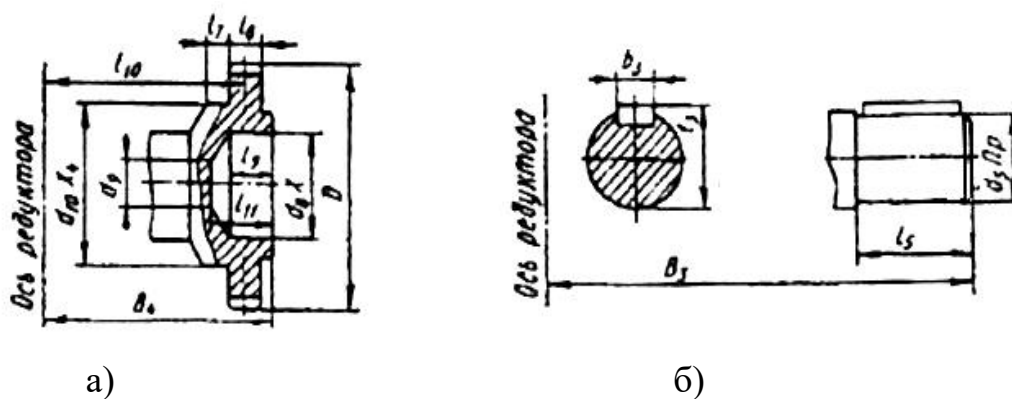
Общий вид концов валов редуктора Ц2, а – тихоходного; б – быстроходного
